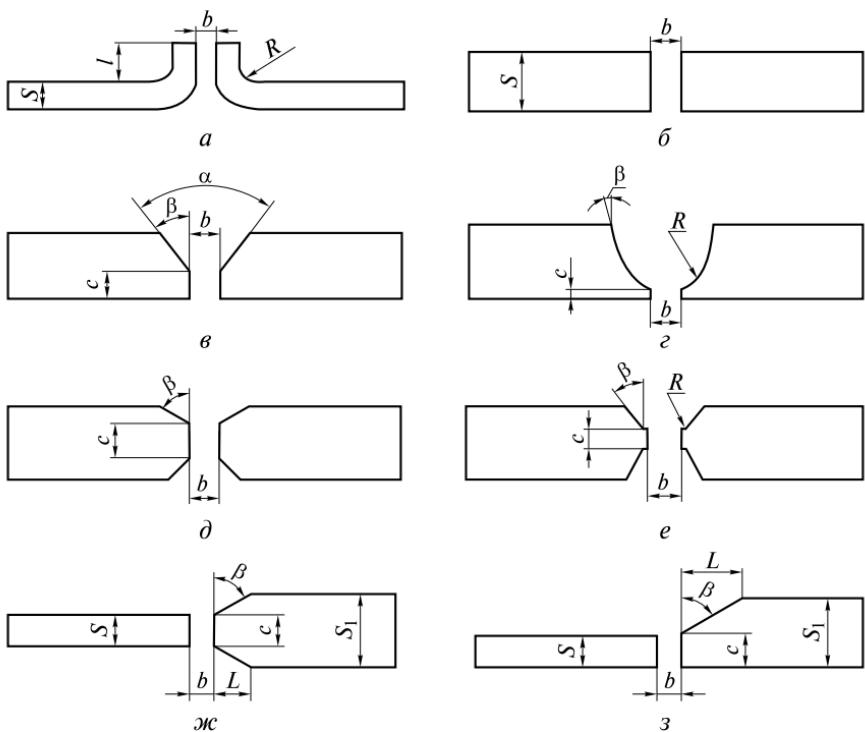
Примеры (а—з) формы кромок, подготовленных под сварку:
